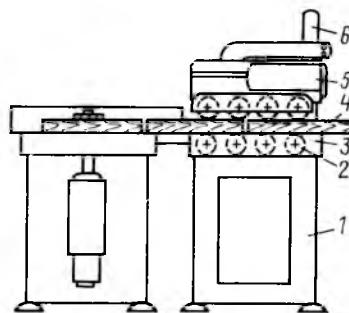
Схема установки автоподатчика к фрезерному станку для закругления кромок в передних ножках стула
